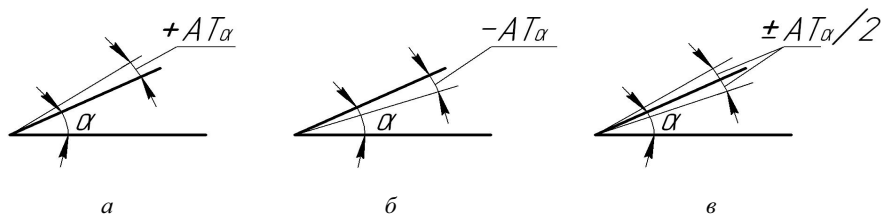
Типы расположения полей допусков для угла призматического элемента:
